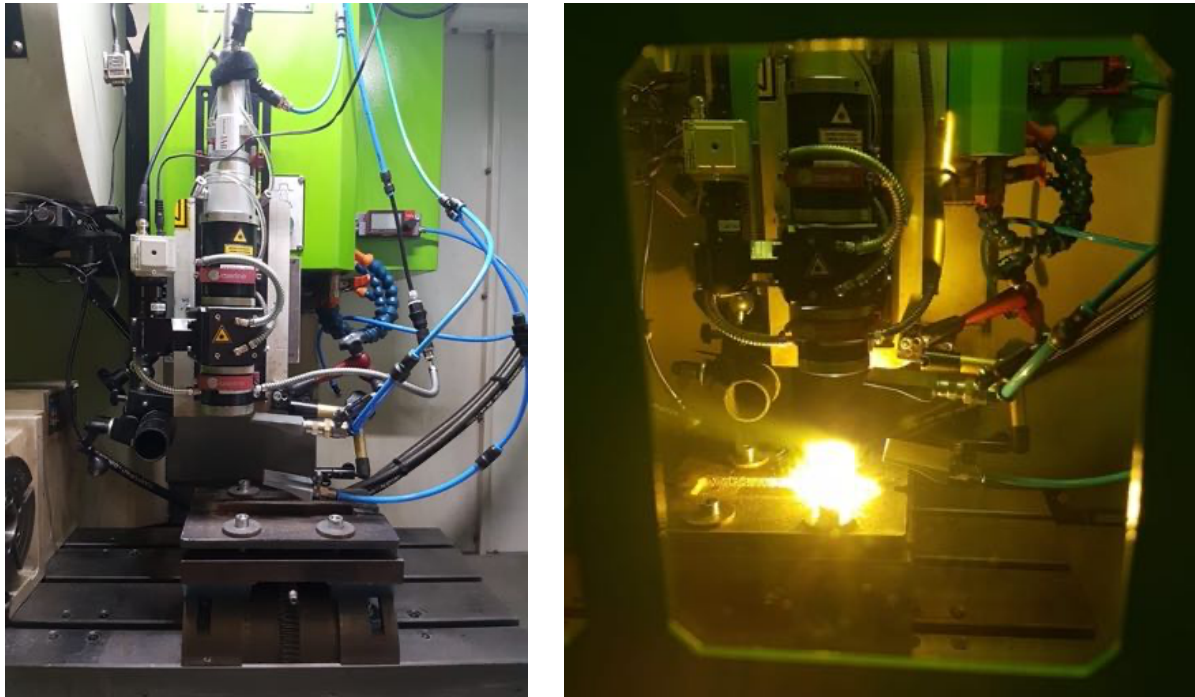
Versuchsaufbau (links) und Schweißprozess (rechts)
